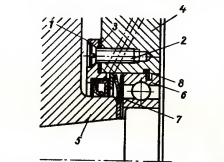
Осевая стабилизация коленчатого вала двигателя P-60.
